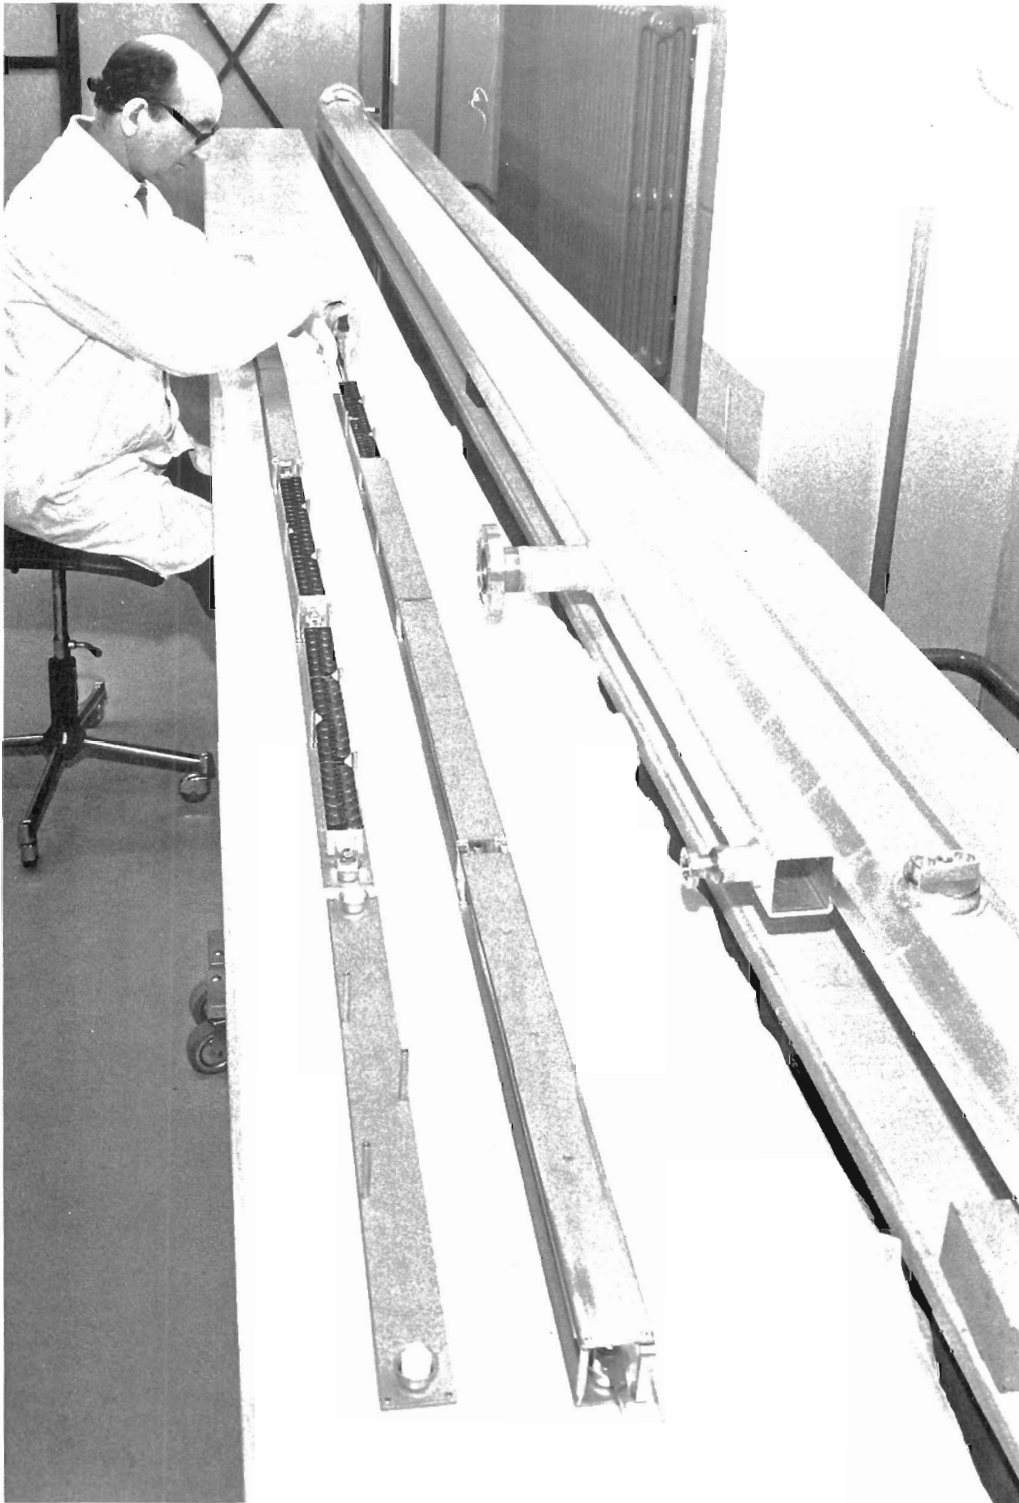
Prototyp Vakuumkammer und Pumpenmontage
